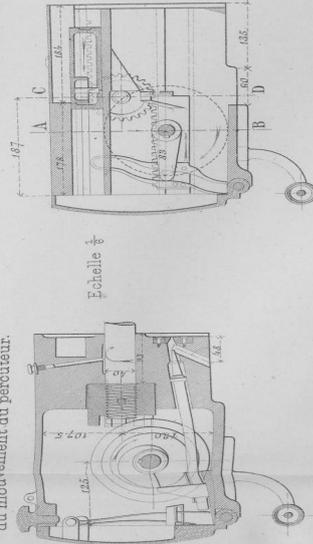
Coupe par l'axe du pignon transmettant le mouvement de l'extracteur au piston chargeur, de l'arbre chétoie suivant AB de la fig. 8 et vue d'ensemble du mécanisme intérieur.
